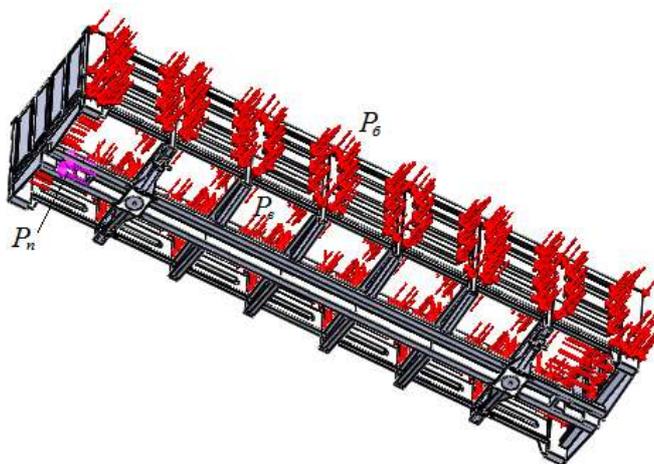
Компьютерная модель прочности несущей базовой конструкции полувагона с приложенными нагрузками
